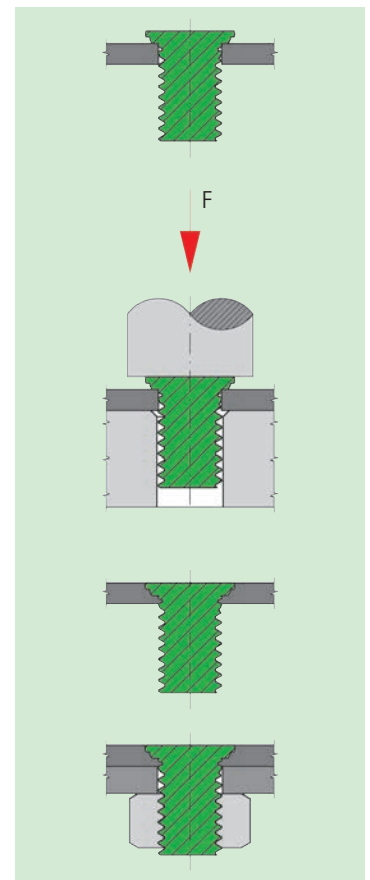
Einpress-Gewindestift Clifa®-SP Bild 8
